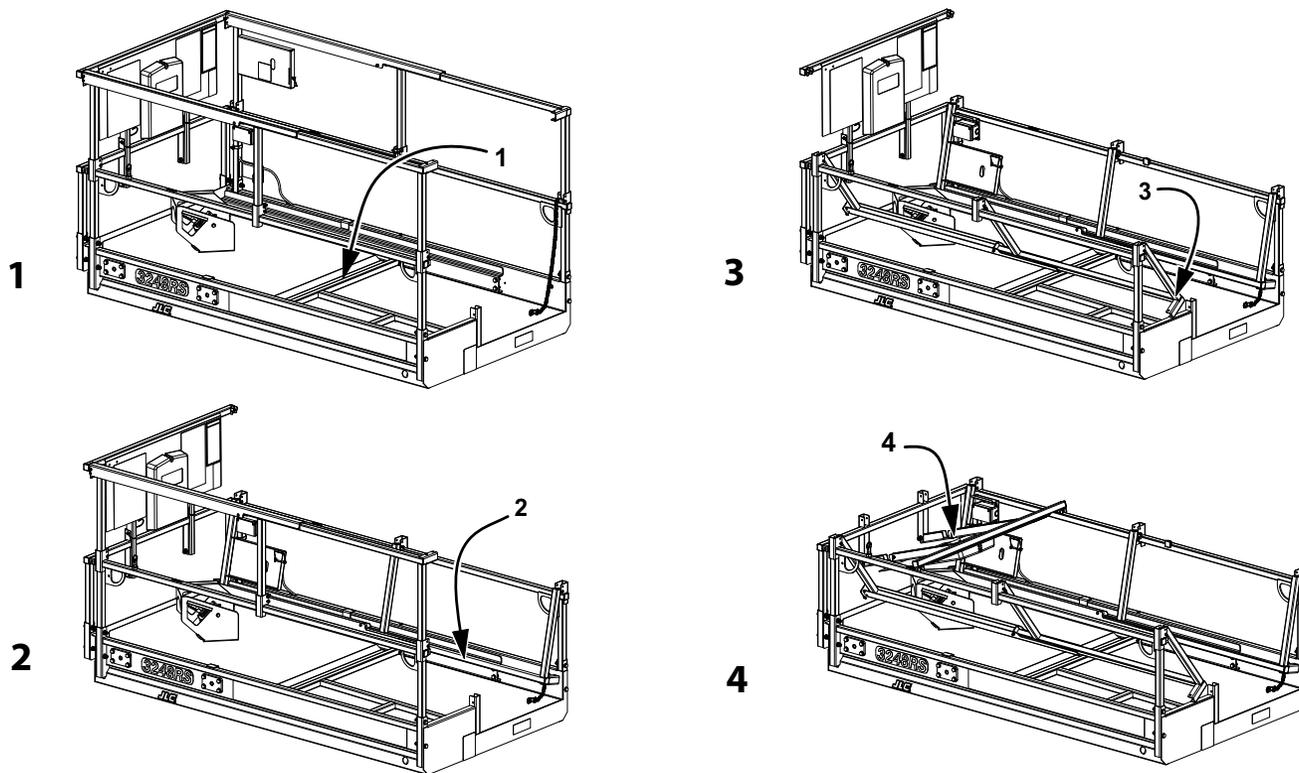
Barandillas de la plataforma - Secuencia de plegado - (3248RS/10RS SOLAMENTE)
